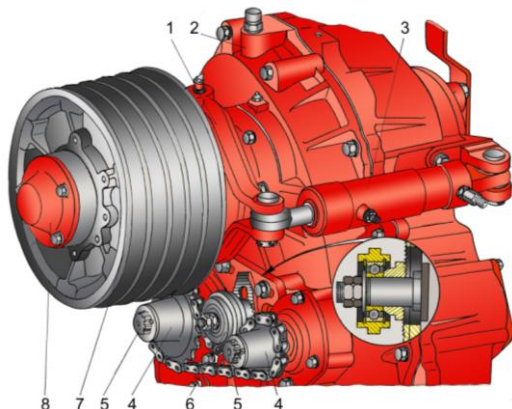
Привод питающего аппарата комбайна КСК-600: 1 – рычаг включения фрикционной муфты; 2 – корпус коробки передач; 3 – гидроцилиндр; 4 – сменные звездочки (ведущая – слева, ведомая – справа); 5 – валы для установки сменных звездочек; 6 – натяжное устройство; 7 – шкив; 8 – крышка
